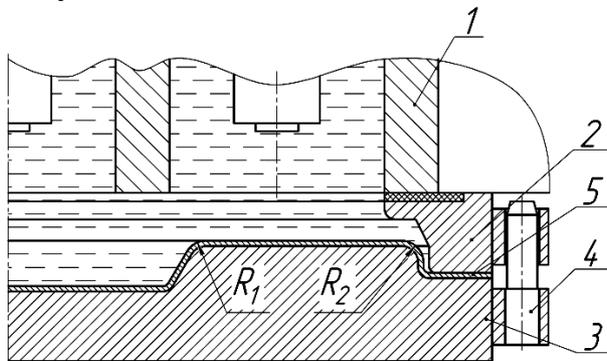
Схема калибровки на пуансон: 1 – разрядный блок; 2 – прижимное кольцо; 3 – пуансон; 4 – центровочные штифты; 5 – заготовка
